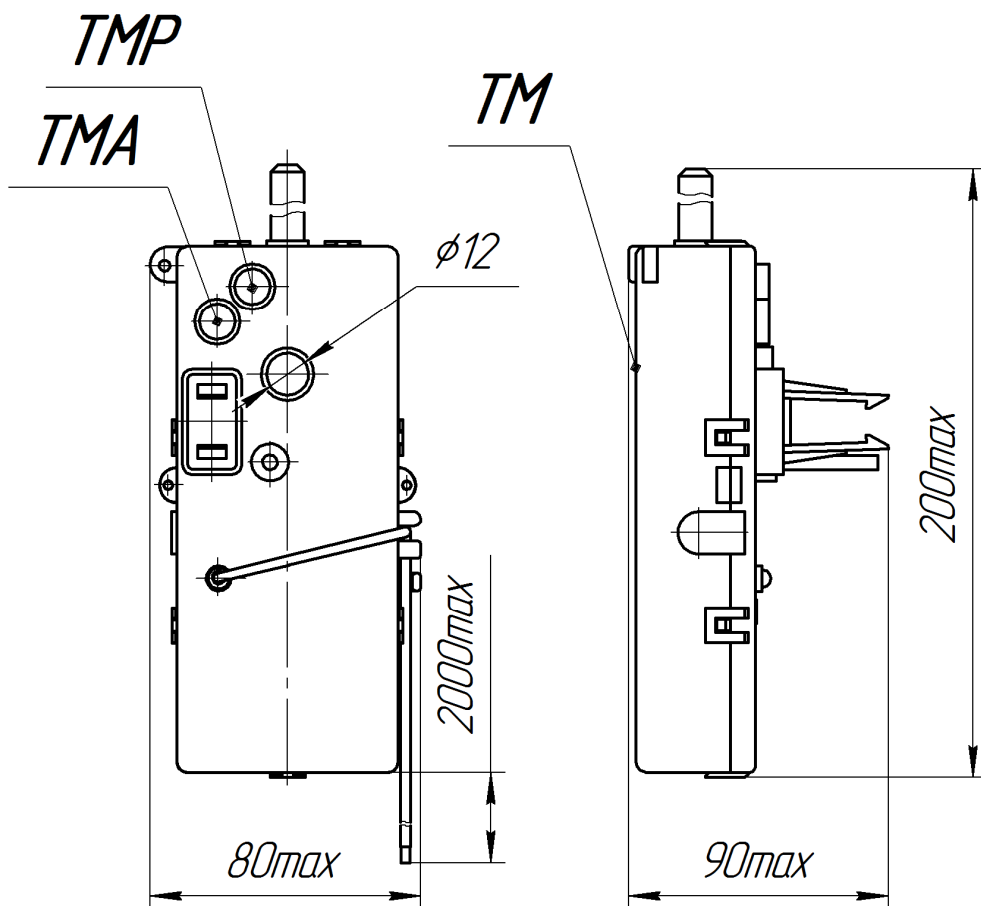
Габаритные, установочные размеры и расположение индикаторов счетчиков, РИМ 189.21–01, РИМ 189.23–01 в корпусе «Тип I»
